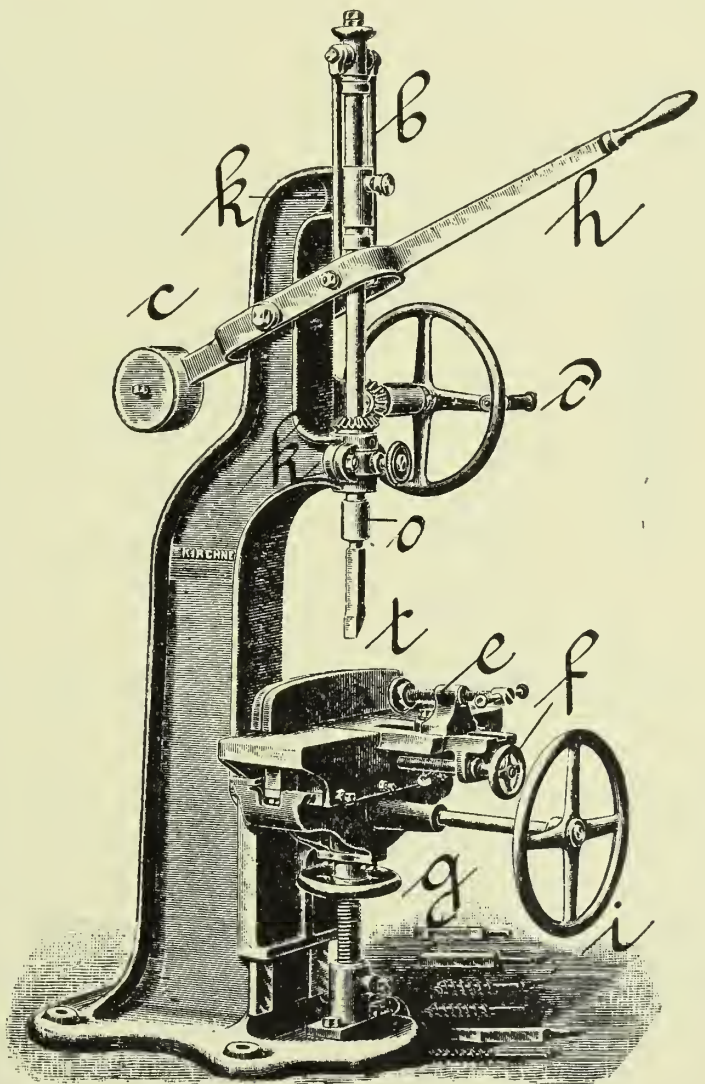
Stemmaschine, verbunden mit Bohrmaschine, von Kirchner & Ko. in Leipzig.
